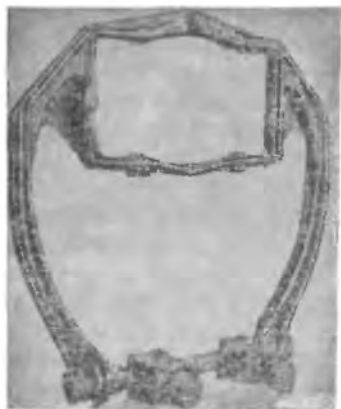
Отливка из алюминиевого сплава. Масса отливки 4,9 кг
